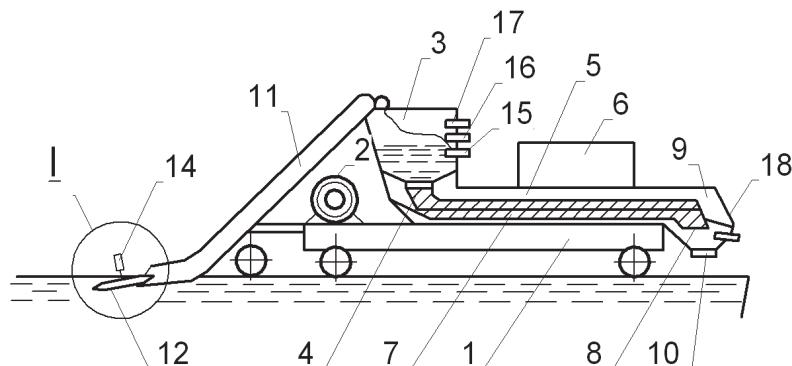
Общий вид установки для СВЧ-обработки почвы
